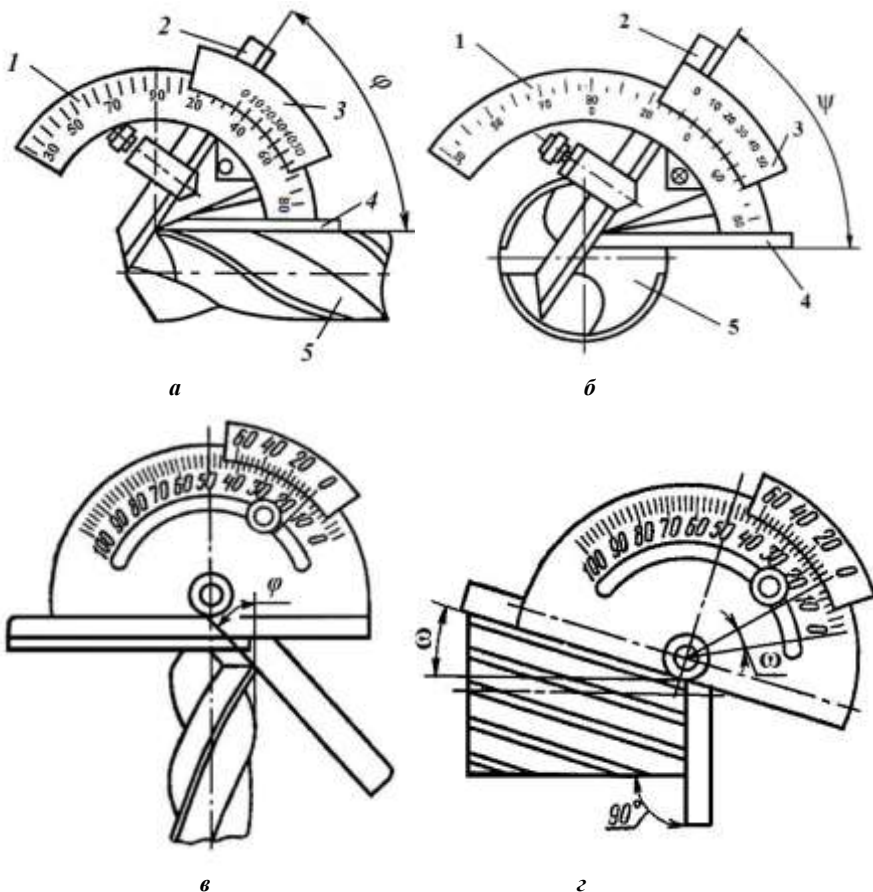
Вимірювання кута при вершині свердла φ (а), кута нахилу поперечної кромки свердла ψ (б), кута в плані φ (в) зенкера і кута нахилу гвинтової канавки циліндричної фрези ω (г) універсальним кутоміром
